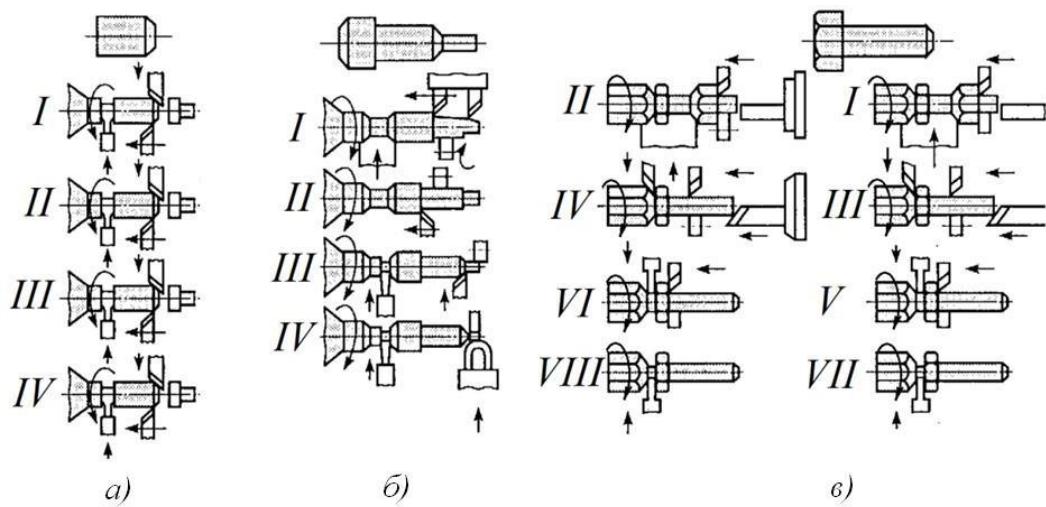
Схема багаторізцевої обробки [3]
